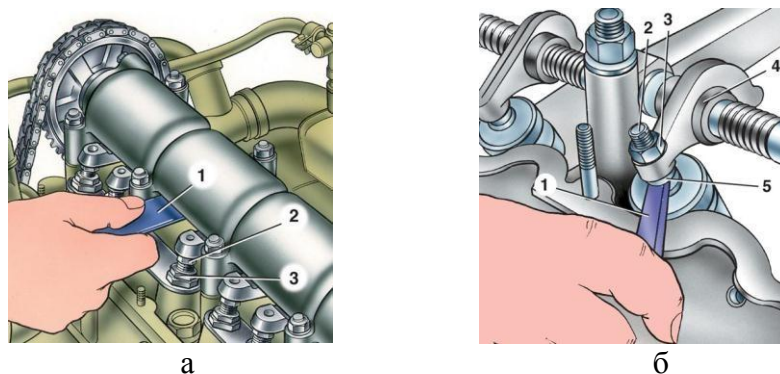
Проверка теплового зазора в ГРМ: а – ГРМ с роликовыми рычагами (рокерами); б – ГРМ с двухплечими рычагами (коромыслами); 1 – щуп; 2 – регулировочный винт; 3 – контргайка регулировочного винта; 4 – коромысло; 5 – наконечник нажимного винта
